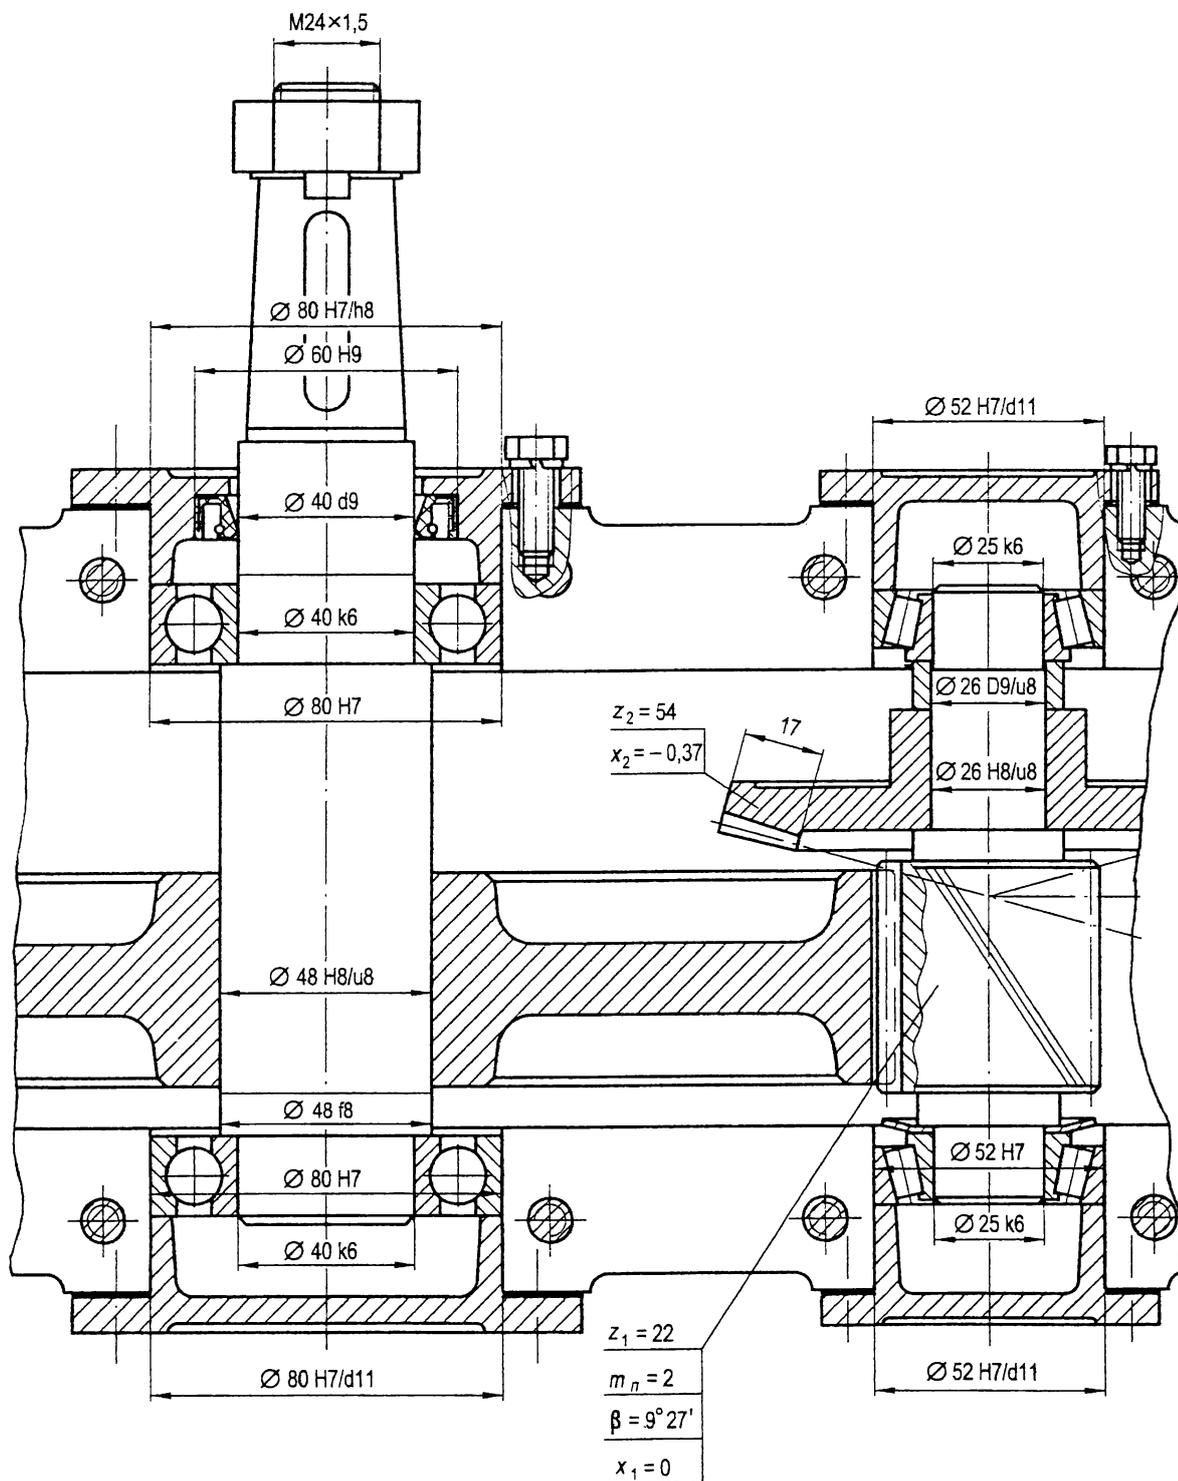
Пример конструкции подшипниковых узлов валов, зафиксированных по схеме «враспор» (крышки подшипников - привертные) [4]
